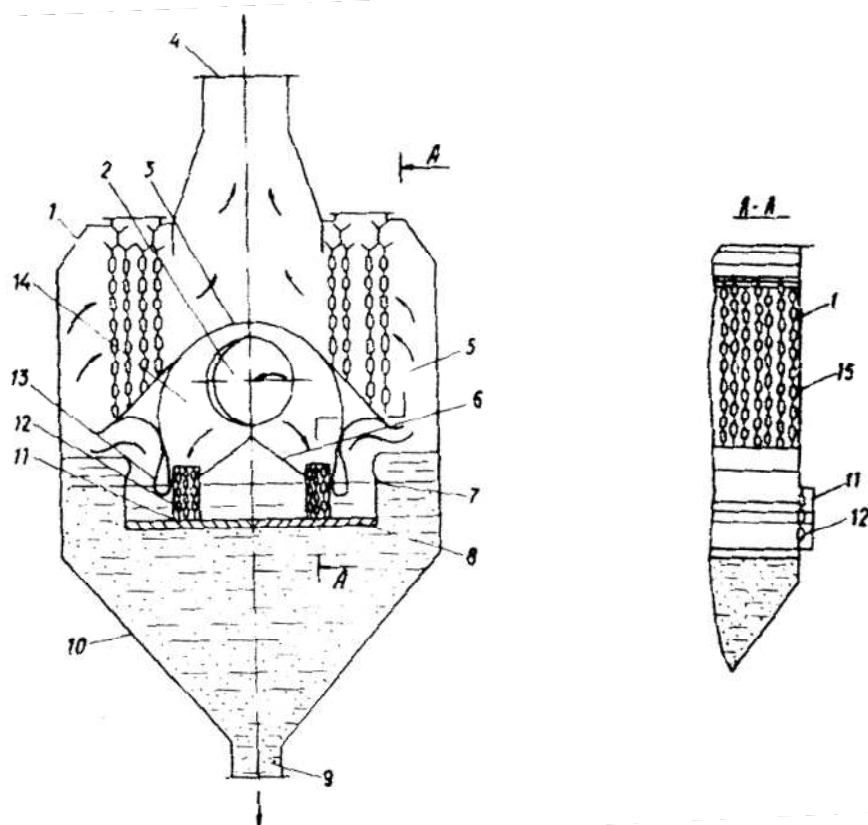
Мокрый пылеуловитель конструкции НИПИОТстрома: 1-корпус; 2-входной патрубок; 3-лерегорodka; 4-выходной патрубок; 5-камера очищенного газа; 6-отражательные пластины; 7- нижняя перегородка; 8-жалюзийная решетка; 9-патрубок для удаления шлама; 10-бункер для сбора уловленной пыли; 11-карман; 12-зашторенные свободно висящие цепи; 13-верхняя перегородка; 14-камера запыленного газа; 15-каплеуловитель
